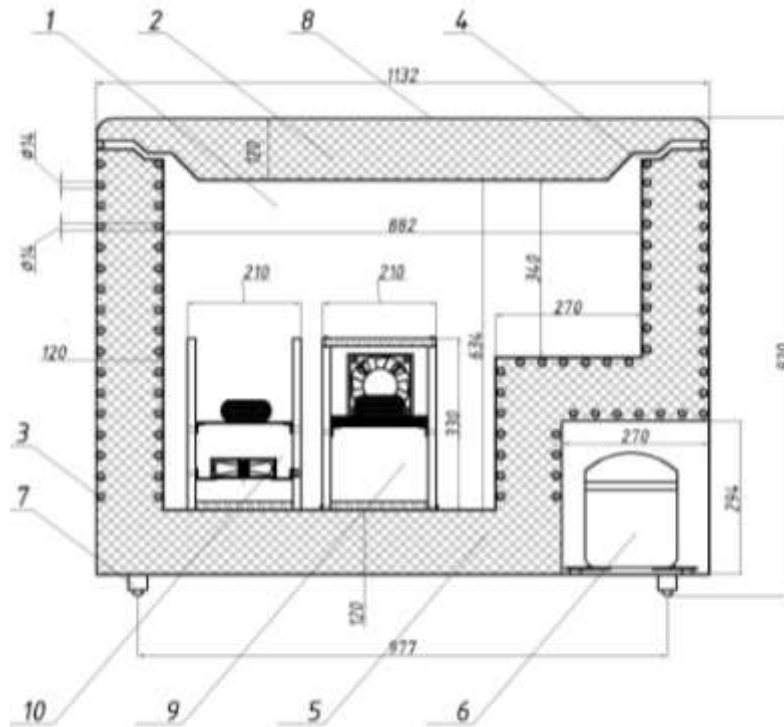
Лабораторный стенд: 1 – камера скороморозильного ларя; 2 – крышка скороморозильного ларя; 3 – конденсатор; 4 – испаритель; 5 – изоляционный слой; 6 – компрессор; 7 – колесная опора; 8 – корпус; 9 – туннельная конструкция со столом-плитой; 10 – туннельная конструкция с сетчатым столом
